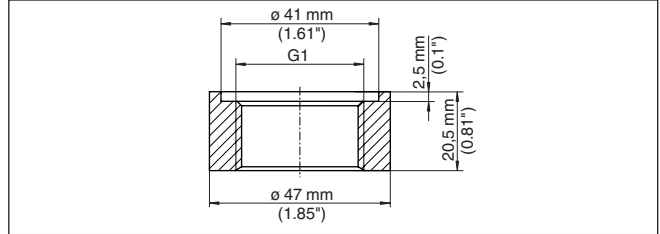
Maße Einschweißstutzen Gewinde G1 (DIN 3852-X)
